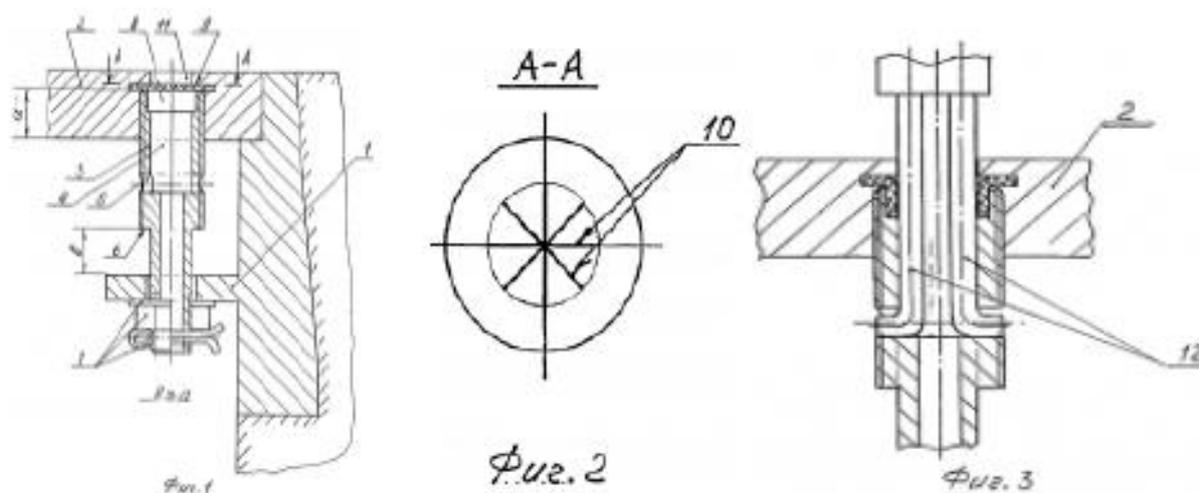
Запорное устройство люка колодца конструкция Образцова Д.И. и Колеганова А.Д.
